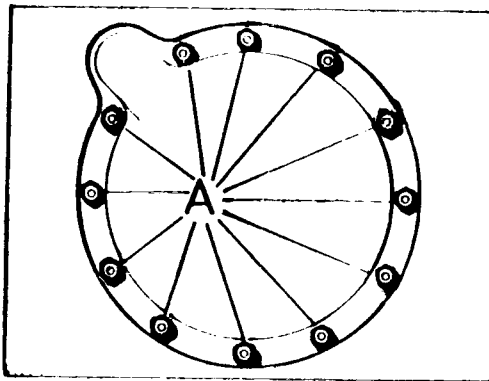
Desmontaje de tuercas de unión caja de cambios a motor
